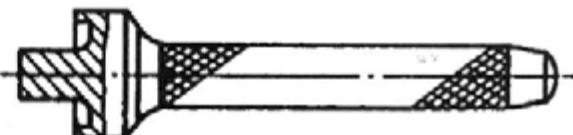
Оправка для выпрессовки сайлент-блока нижнего рычага
